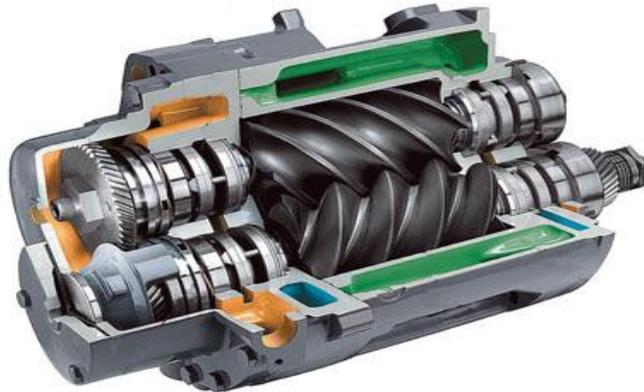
Винтовой компрессор в разрезе (вид на роторы).
